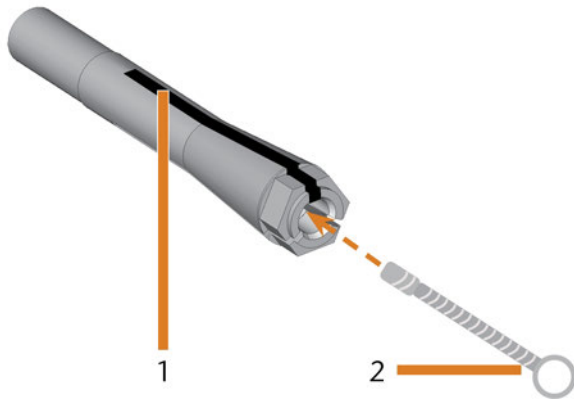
PULIZIA DELLA PINZA DI SERRAGGIO
